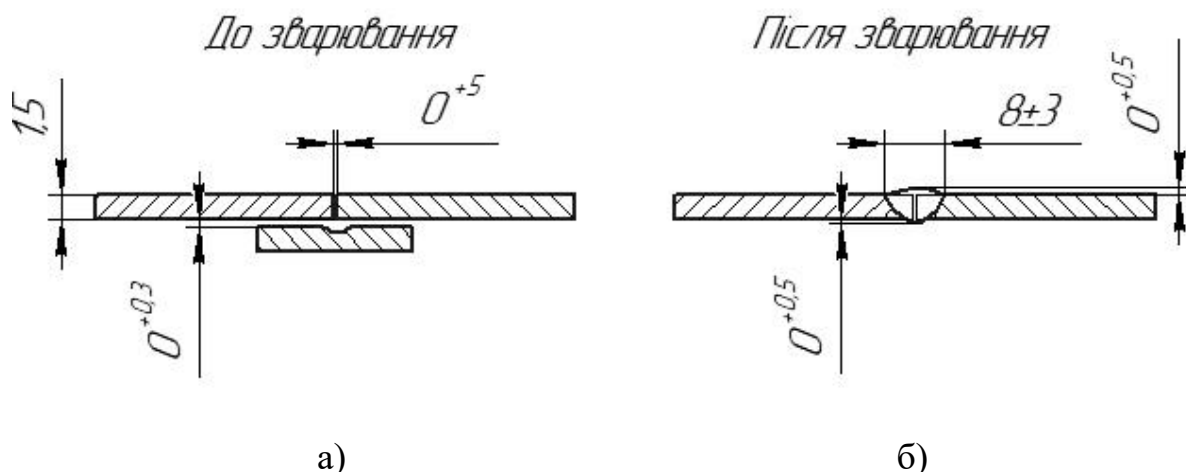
Підготовка кромки під зварювання (а) і готовий зварний шов (б)
